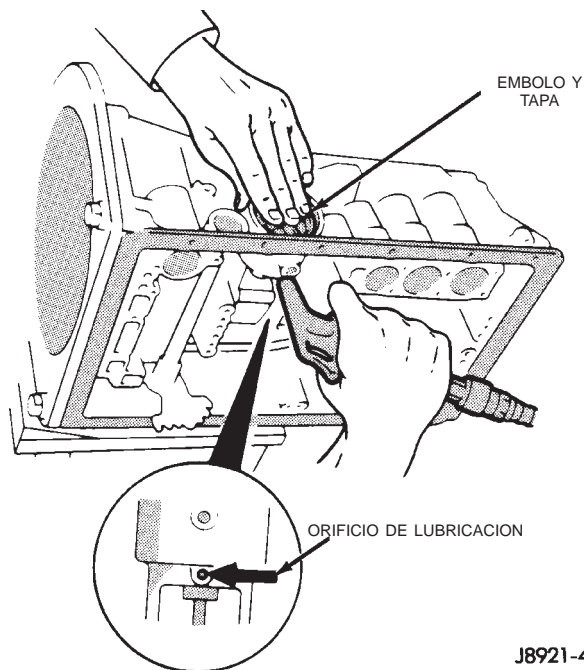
Desmontaje de la tapa del servomecanismo y émbolo
